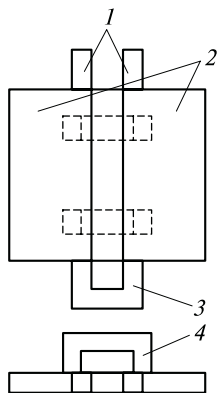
Сборка стыковых соединений под электрошлаковую сварку:
